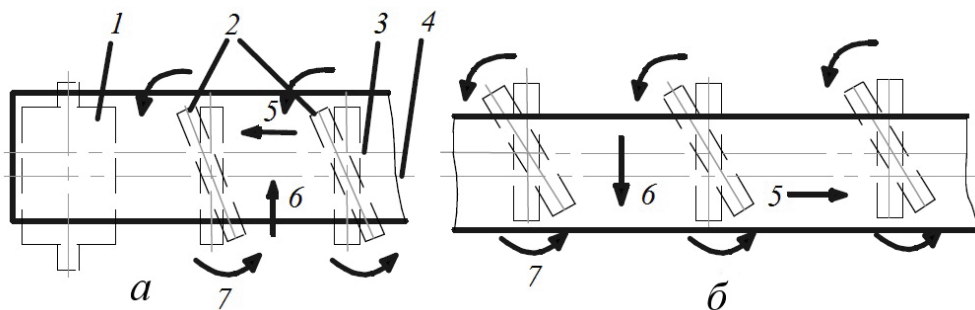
Регулировка верхних роlikоопор ленточного конвейера при сходе ленты: *а* — с приводного барабана; *б* — в средней части; 1 — приводной барабан; 2 — роlikоопоры; 3, 4 — оси ленты и конвейера; 5, 6, 7 — направления движения ленты, ее схода и разворота роlikоопор
